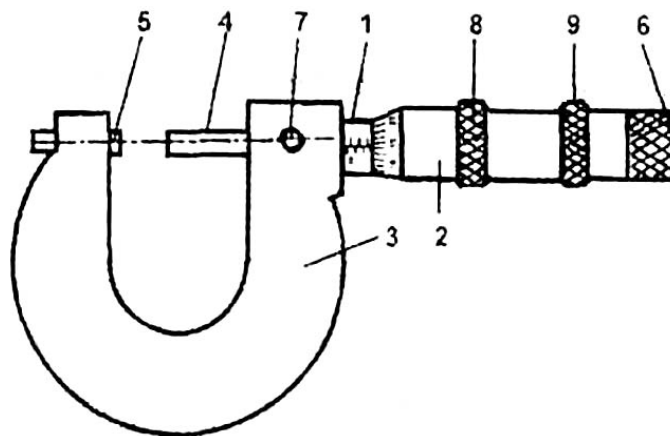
Устройство микрометра МК: 1 – стержень; 2 – барабан; 3 – скоба; 4 – измерительный стержень; 5 – пятка; 6 – трещотка; 7 – стопор измерительного стержня; 8 – накатное кольцо барабана; 9 – стопорная гайка барабана
